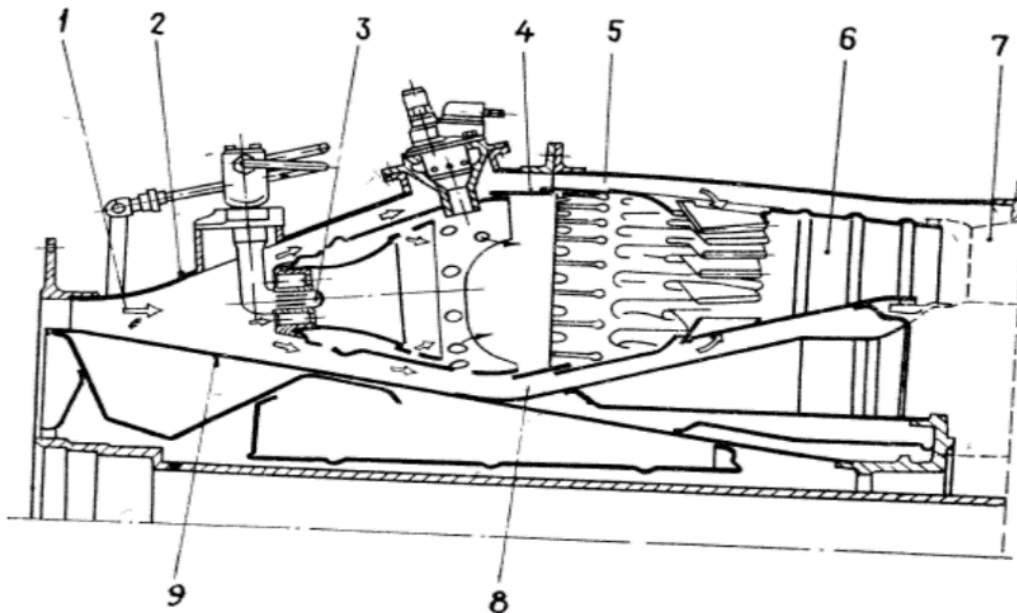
Эскиз кольцевой камеры сгорания: 1 – поток воздуха; 2 – наружный корпус; 3 – форсунка; 4 – кольцевая жаровая труба; 5 – наружный кольцевой канал; 6 – газосборник; 7 – сопловой аппарат турбины; 8 – внутренний кольцевой канал; 9 – внутренний корпус.
